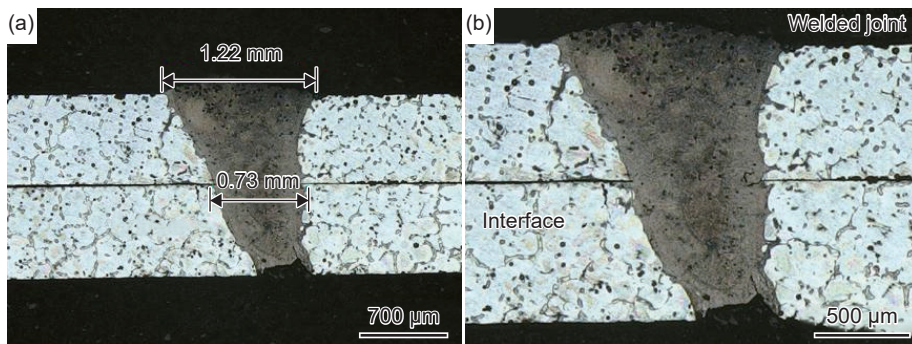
焊缝截面形貌 (a) 焊缝截面; (b) 熔化区放大图
